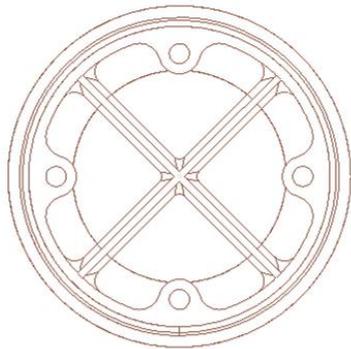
esbozo de pieza con bolsillos para cuchillo de 4 cortes
